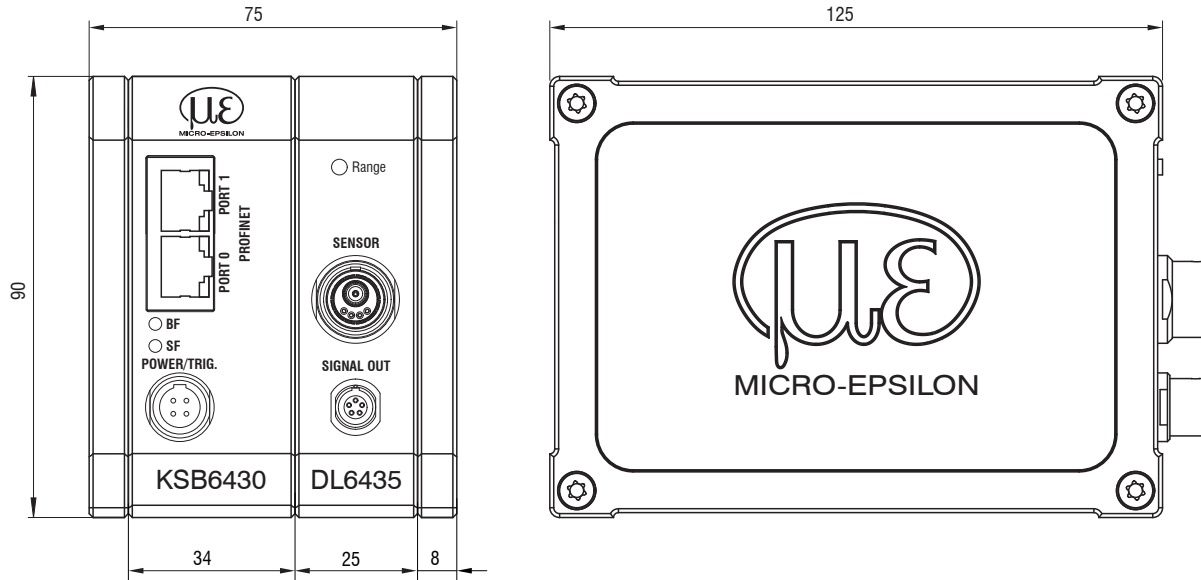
Maßzeichnung Controller mit Basiseinheit, Demodulator und Gehäusedeckel, Abmessungen in mm
